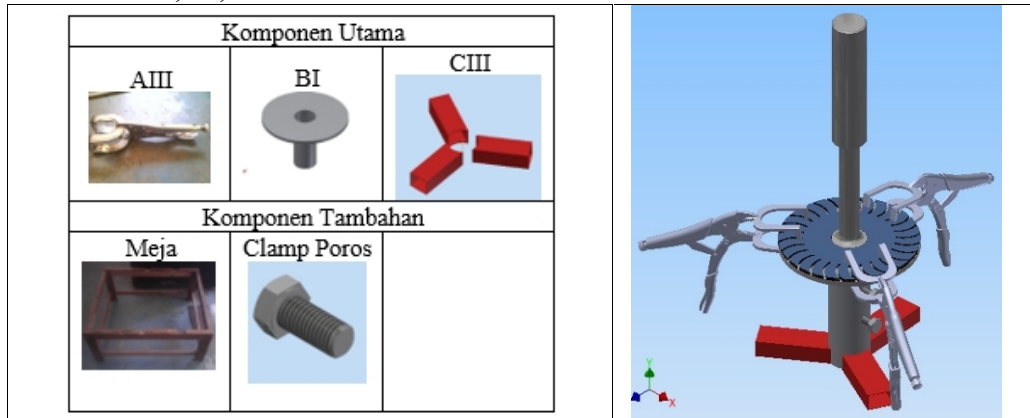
Alternatif ke-2 *assembly fixture* perakitan *runner*.
